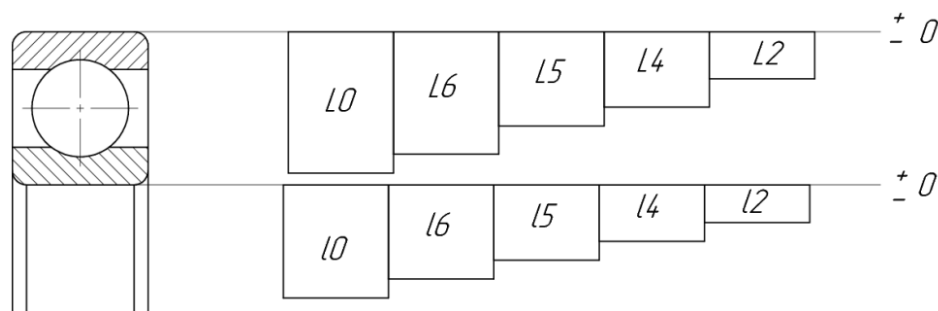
Схема расположения полей допусков на присоединительные размеры подшипников качения различных классов точности
